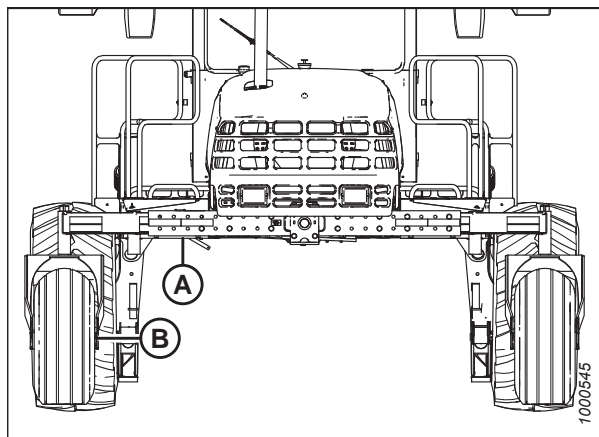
Опорные колеса и балансир (вид в положении двигателем вперед)
